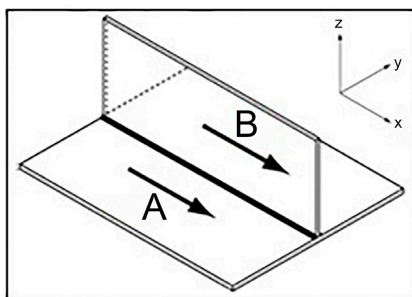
Etapas do Experimento: Etapa A (Soldagem do cordão 01) e Etapa B (Soldagem do cordão 02). Setas indicam sentido de soldagem.
